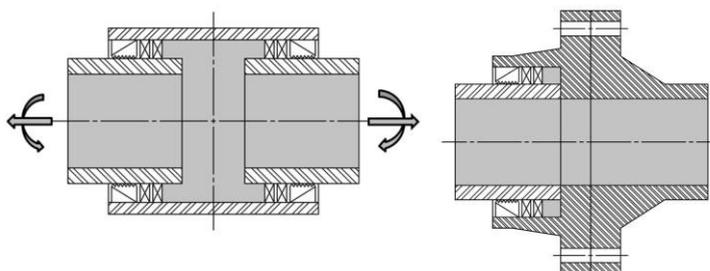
Слева: тип соединителя с двойным захватом и уплотнением. Справа: соединитель фланцевого типа
